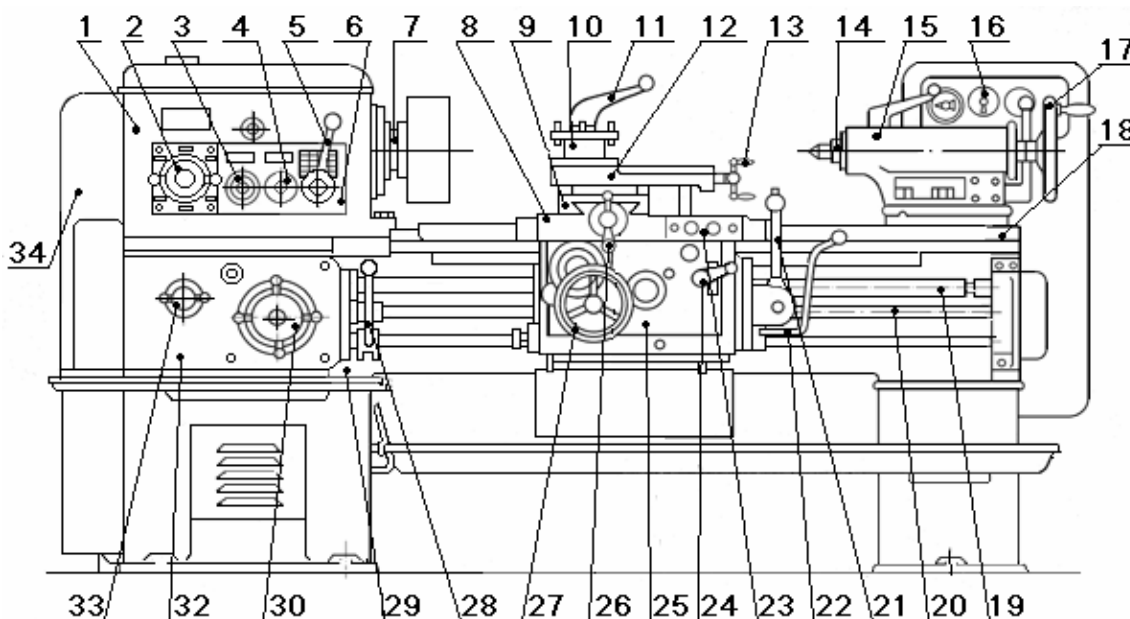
Токарно-винторезный станок модели 1К62:
